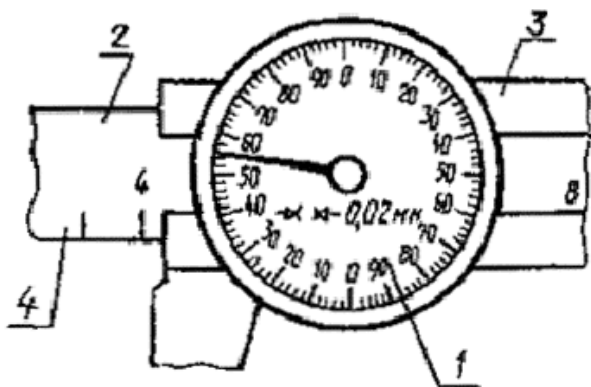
Конструкція та будова штангенциркуля ШЦК: 1 – кругова шкала відлікового пристрою; 2 – штанга; 3 – рамка; 4 – шкала штанги
